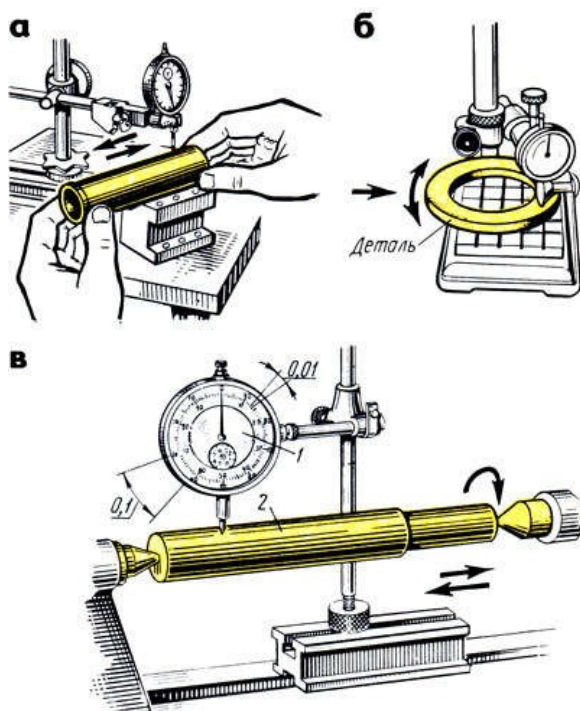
Приемы проверки индикатором: а, б - перемещением деталей, в - в центрах; 1 - индикатор, 2 - деталь
